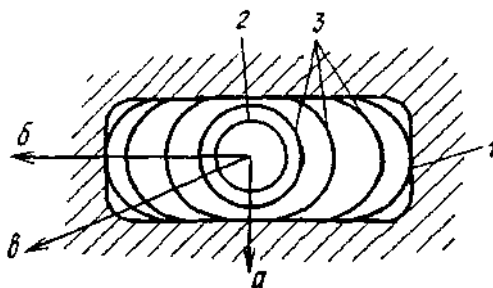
Стадии раздувания цилиндрической заготовки при формировании изделия с сильно различающимися размерами поперечного сечения: a , b , v – направления раздувания (пояснения в тексте); 1 – полуформа; 2 – исходная заготовка круглого сечения; 3 – изменение формы сечения заготовки на различных стадиях раздувания
